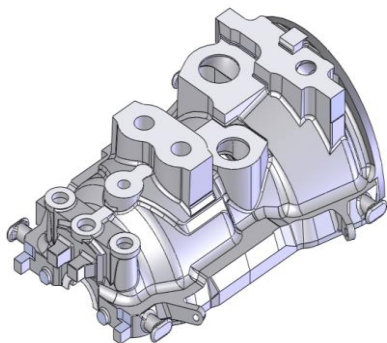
Отливка «нижняя часть корпуса паровой турбины».
